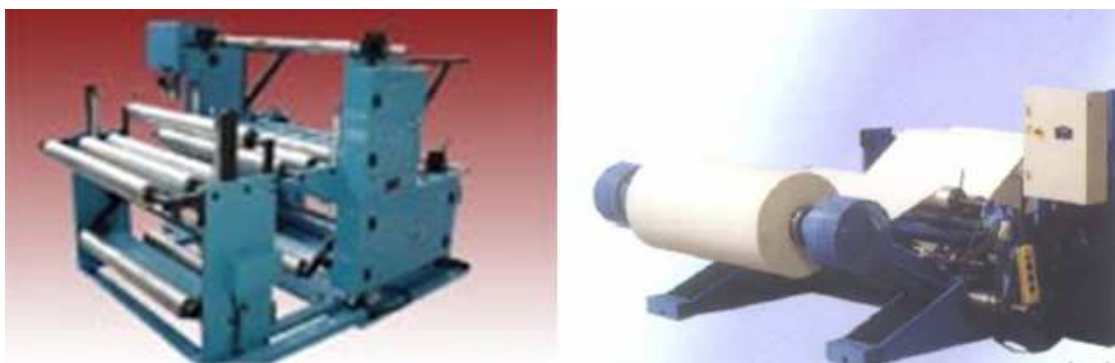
Máquina rebobinadora Central<sup>7</sup>.
